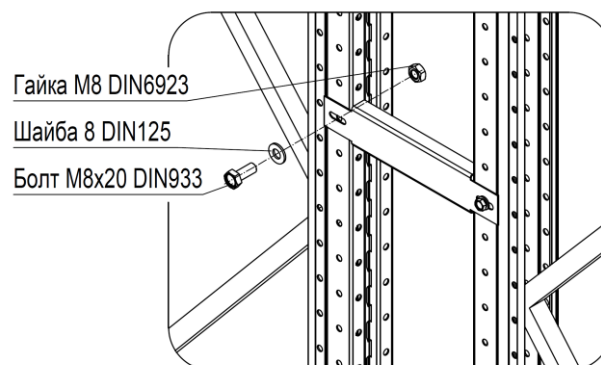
Установка соединителя ряда типа СР.ХХХ.П.
